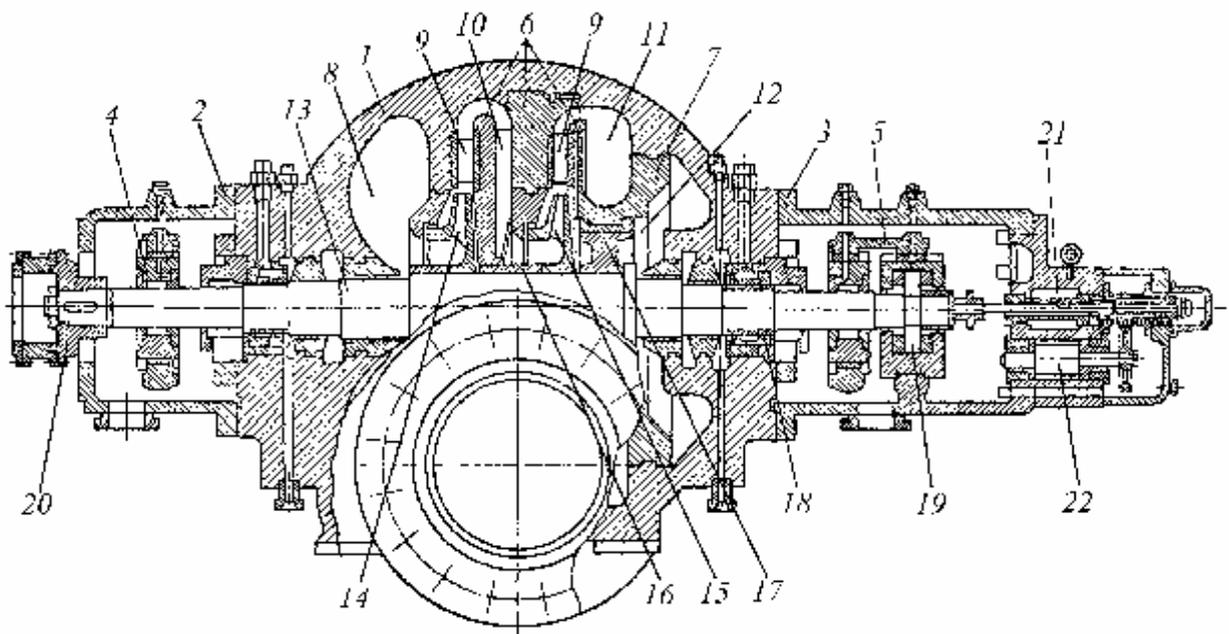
Двухступенчатый центробежный компрессор с горизонтальным разъемом корпуса ГПА-Ц-6,3 [2]
